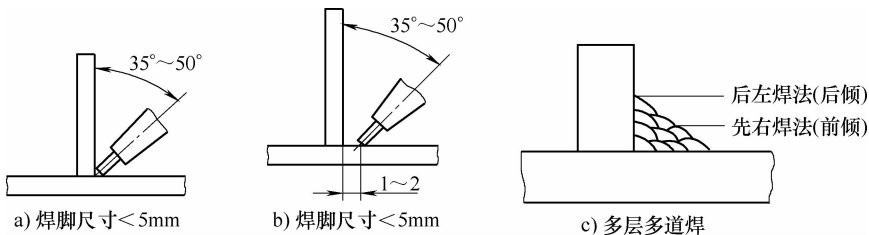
T形接头角焊缝半自动 CO₂ 焊
